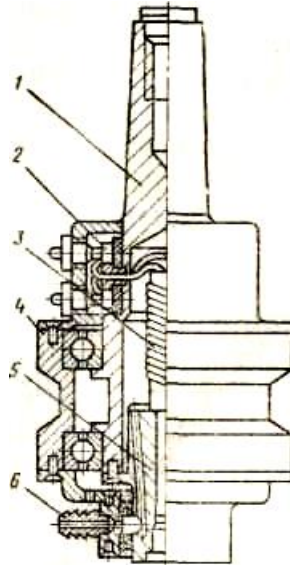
Пристрій універсальної ультразвукової головки: 1 – корпус руховий; 2 – щітка; 3 – обмотка; 4 – корпус нерухомий; 5 – концентратор; 6 – штуцер
